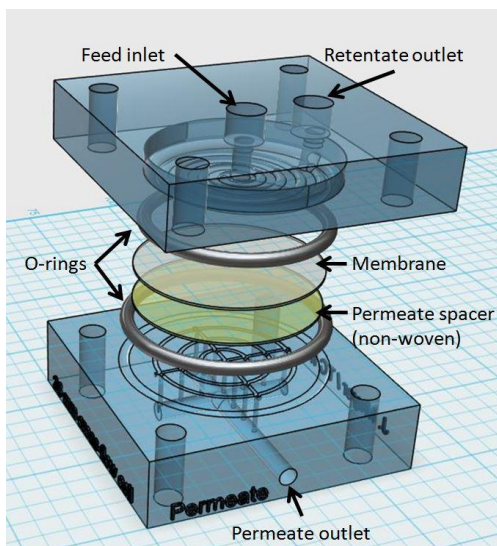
Explosionszeichnung einer Cross-flow Zelle mit O-Ringen, Membranprobe und Permeatspacer aus Vliesstoff.
